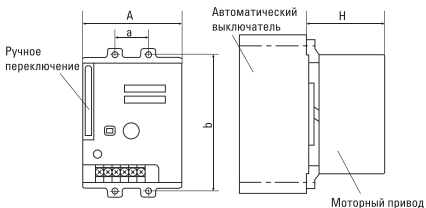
Габаритные размеры моторного привода к ВА-99М 400, 630, 800
